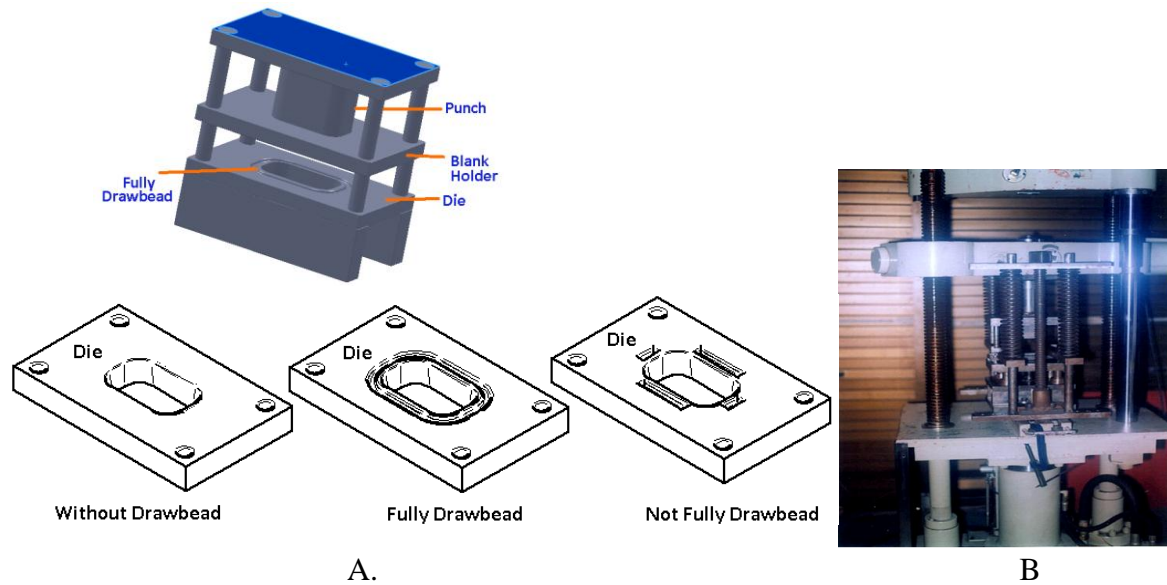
A. Punch and Die Set (without, fully dan not fully drawbead), B. Susunan Punch and Die on press machine.
